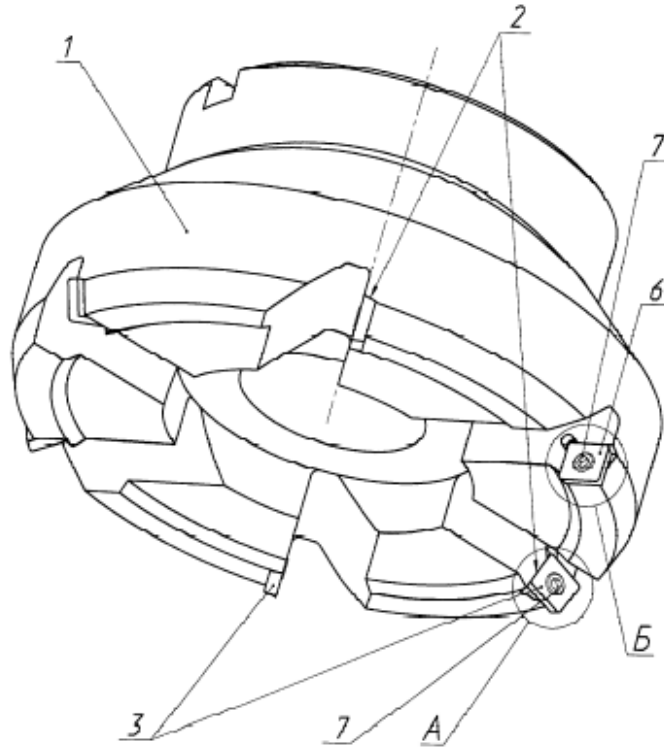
Конструкція збірної торцевої фрези для обробки зовнішніх
